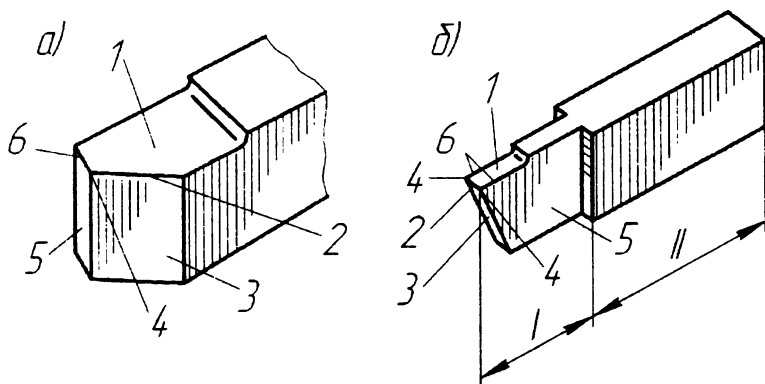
Конструктивные параметры резца: а – проходной прямой; б – отрезной
